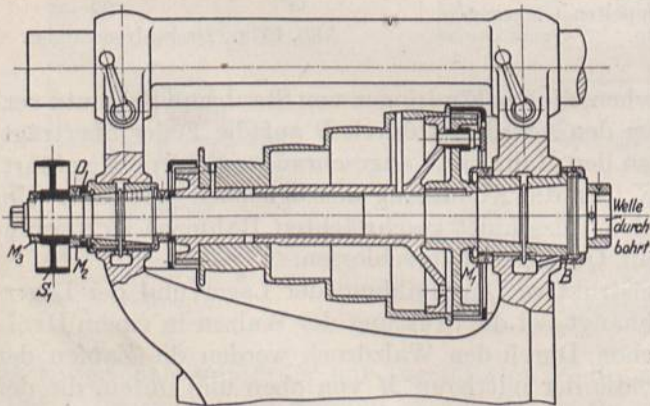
Spindelstock der Hendey-Norton Fräsmaschine. (Nach Hülle, Werkzeugmaschinen).
